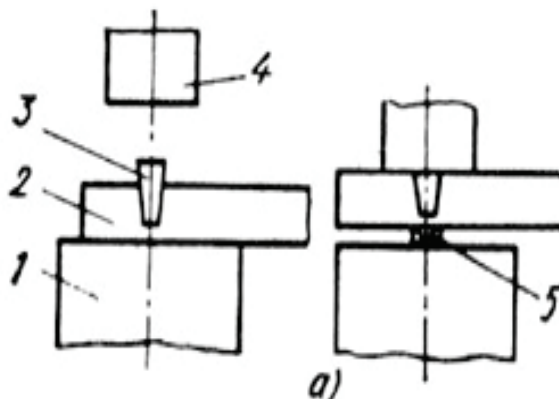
Схема отрубki заготовки с одной стороны топором и квадратом:
